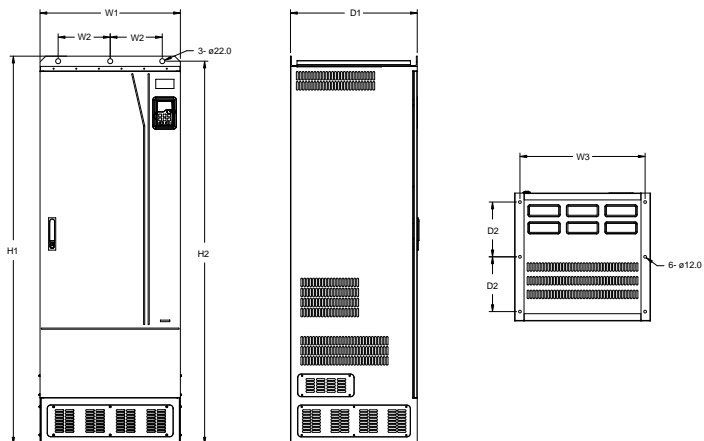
ПЧ 660 В 400–630 кВт, размеры для напольного монтажа
